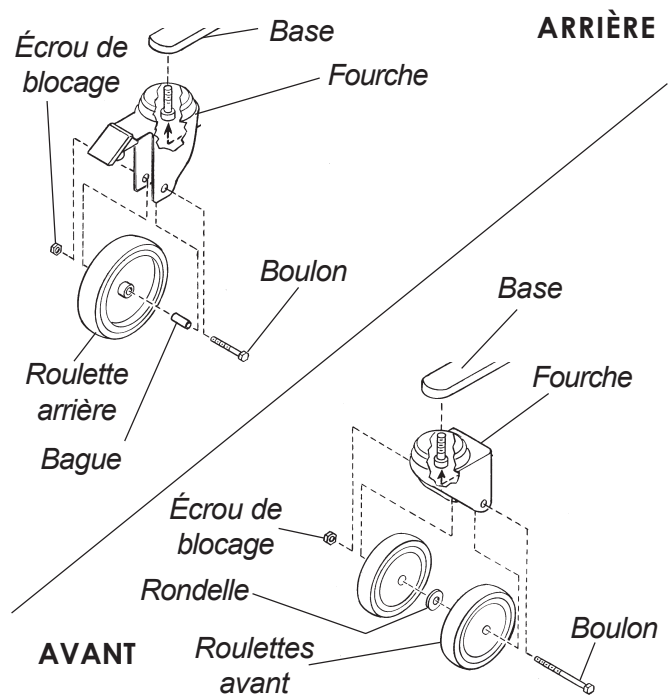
REMPLACER LES ROULETTES OU /ET FOURCHES
